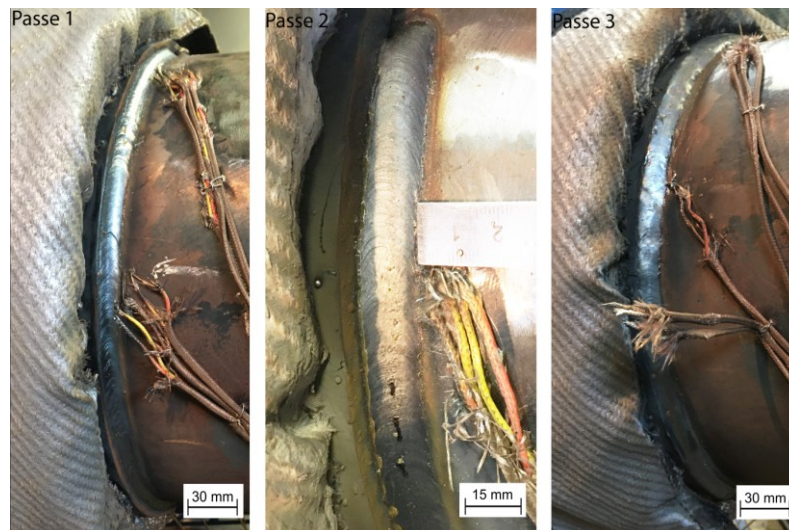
Soldagem orbital mecanizada de dupla calha tipo-B com GMAW-P AC com pré-aquecimento da calha.
